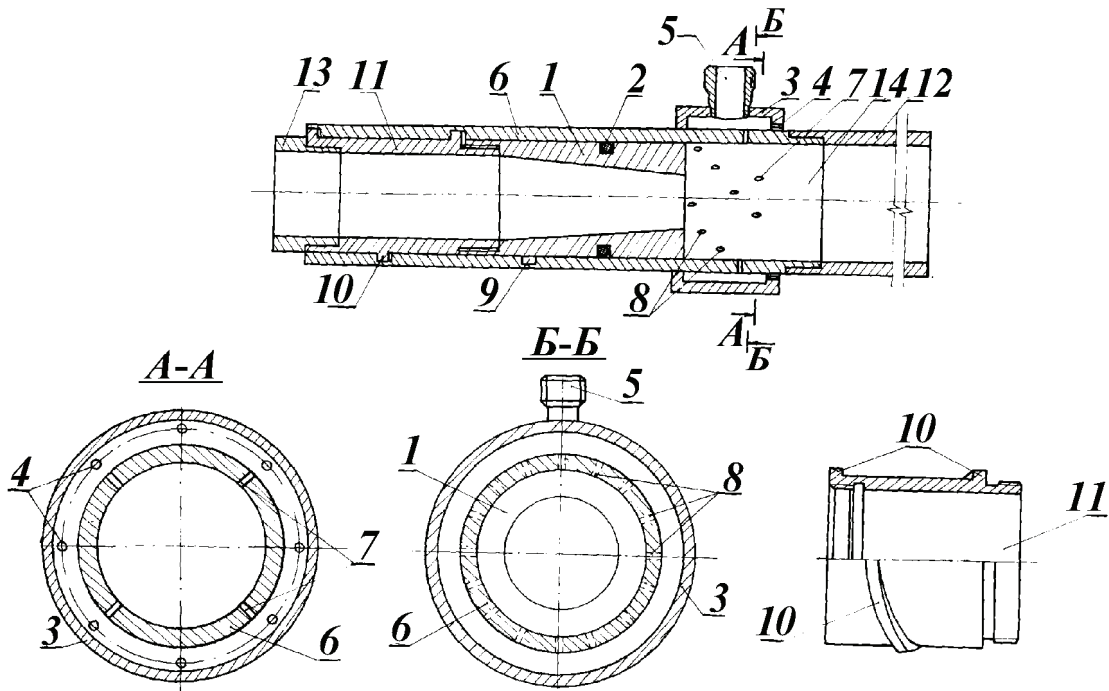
Конструкция устройства для затворения вяжущего и пылеподавления: 1 – конфузор; 2 – сальник; 3 – камера пылегасителя; 4 – калиброванные отверстия; 5 – патрубок; 6 – подвижная обойма; 7 – основные Калиброванные отверстия; 8 – дополнительные Калиброванные отверстия; 9 – винтовая проточка; 10 – винтовой выступ; 11 – фиксатор; 12 – удлинитель; 13 – материальный трубопровод; 14 – камера затворения
